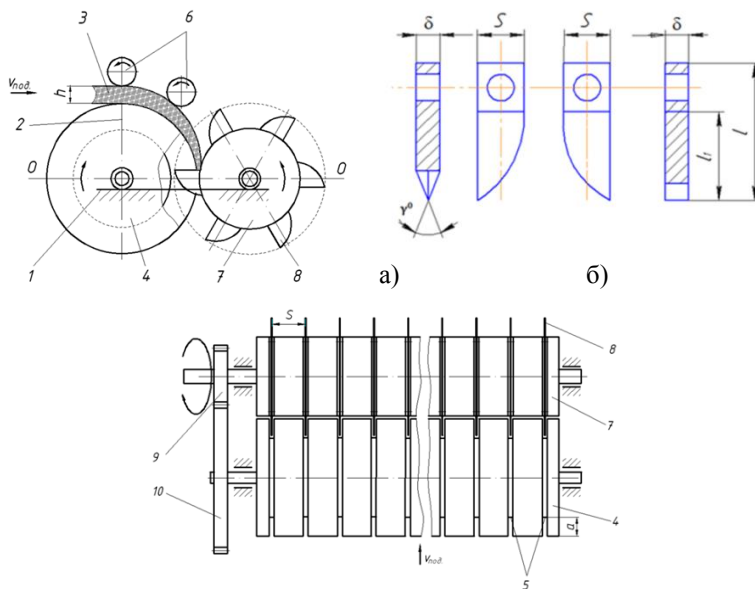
Схема пристрою для руйнування стебел льону олійного: 1 – корпус; 2 – шароформувач; 3 – шар стебел; 4 – подавальний барабан; 5 – щілини – протирізи; 6 – притисні вальці; 7 – ротор; 8 – ножі(а) різального; б) молоткового типу); 9 – ведуча шестерня; 10 – зубчасте колесо
